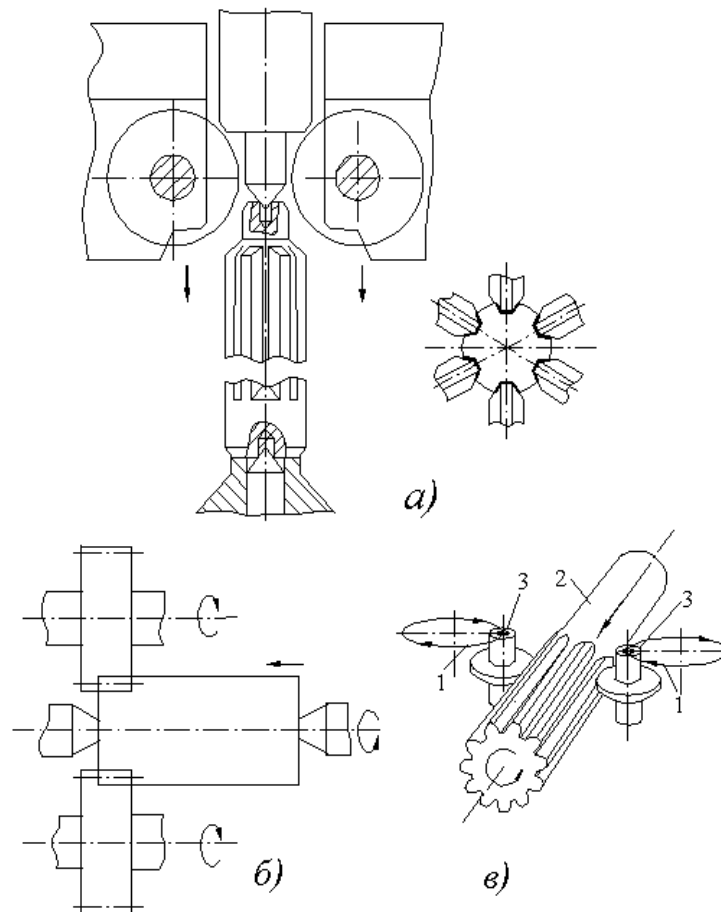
Схемы накатывания шлицев: многороликовой головкой (а); круглыми роликами (б); планетарным методом (в)
